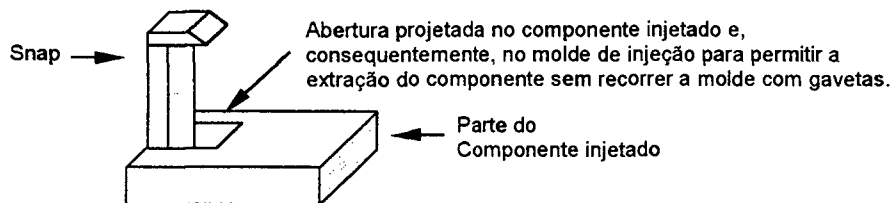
Exemplo de restrição de projeto do molde de injeção - Soluções de projeto para snap, a ser injetado em moldes de injeção isentos de gavetas.
